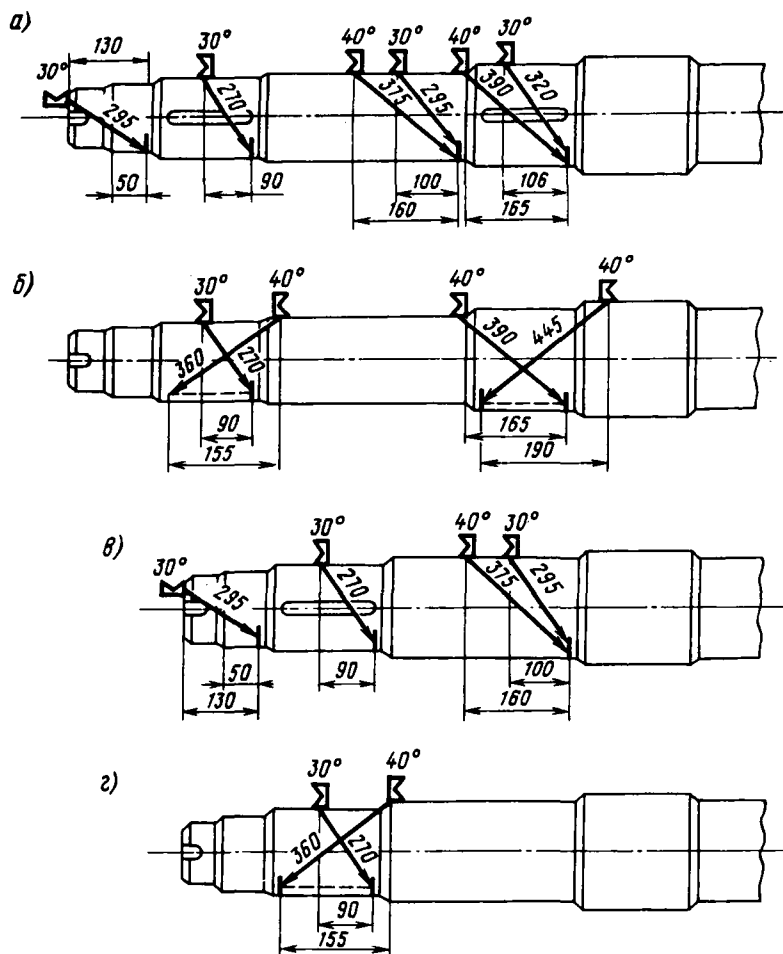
Схемы и зоны контроля наклонными искателями главного приводного вала эскалатора КДС при различном положении искателей (а, б, в, г)
